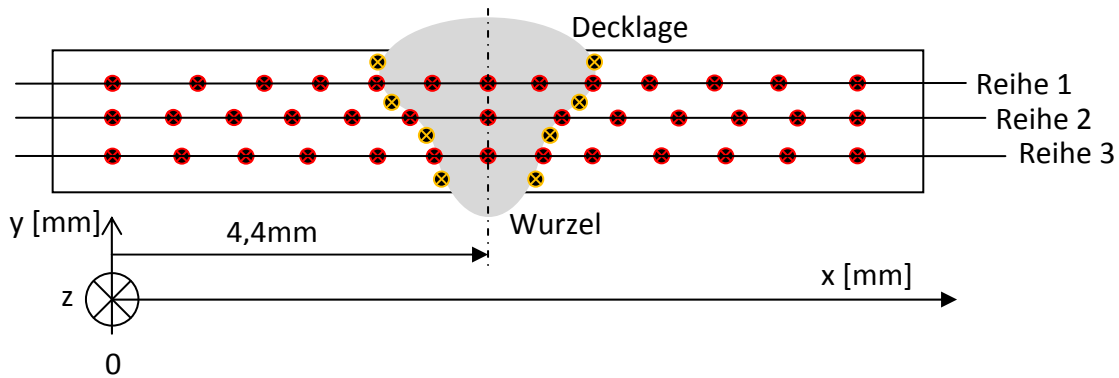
Raster für Härtemessung über einem Querschliff der Schweißnaht
